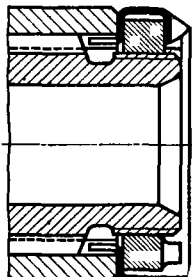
Стопорение кольцевой гайки с торцовыми зубьями чашечной шайбой
